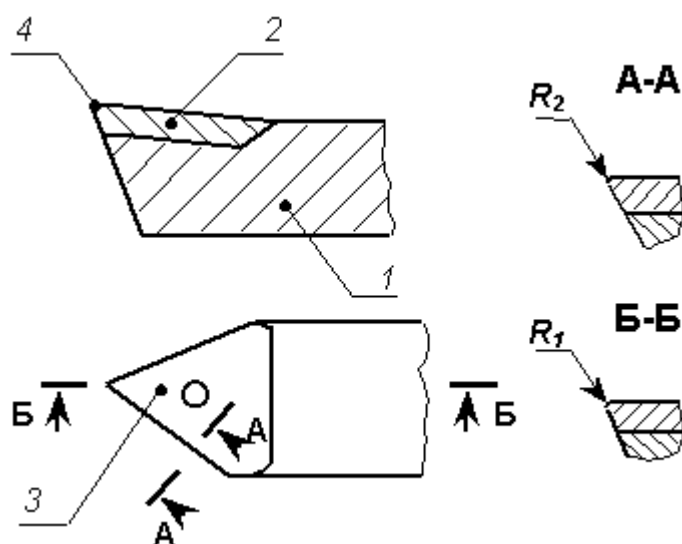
Элементы токарного резца: 1 – резец; 2 – неперетачиваемая пластина; 3 – передняя грань; 4 – вершина резца
